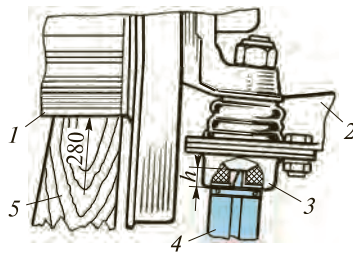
Схема проверки нижнего шарового шарнира:
